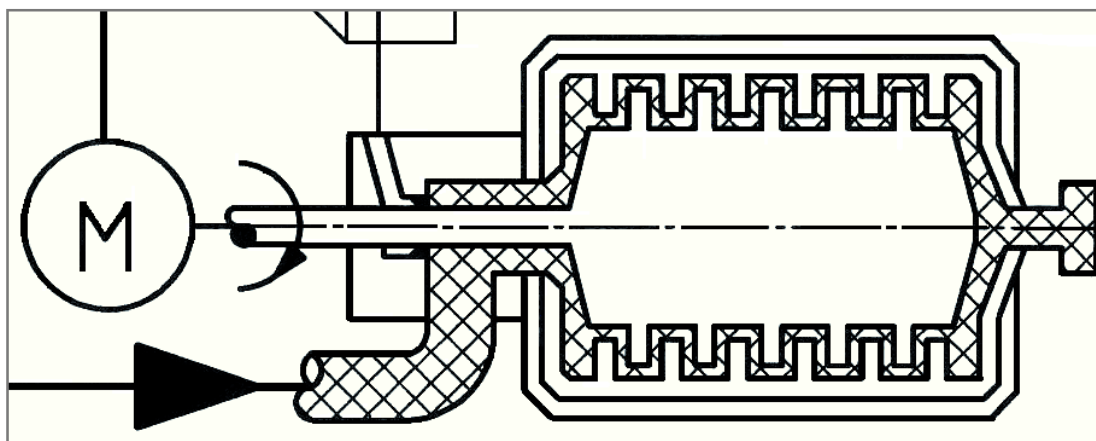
Querschnitt des Mix-Kopfes einer Druckaufschlagmaschine
